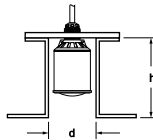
Montage de la rehausse en cas de dimensions de rehausse différente
